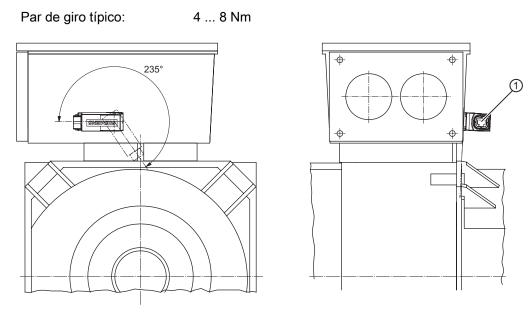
Módulo del transmisor ① montado en la caja de bornes
